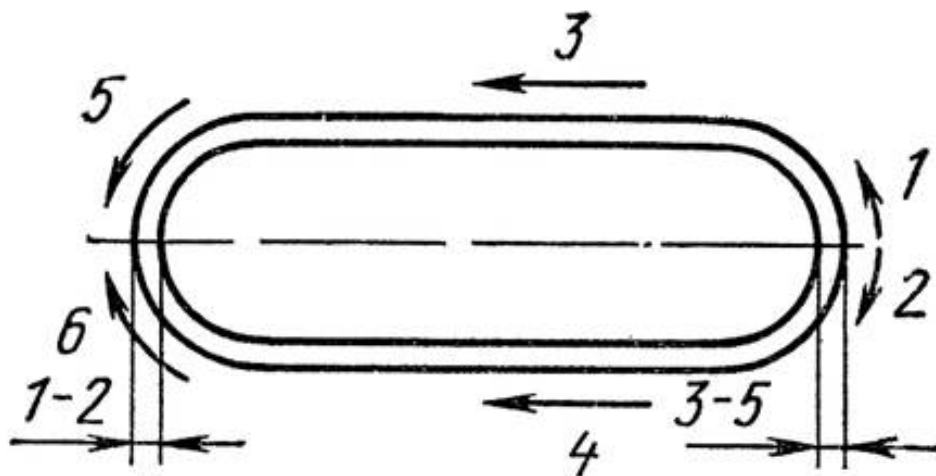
Последовательность выполнения сварного соединения при вварке заплата: 1, 2, 3, 4, 5, 6 – очередность заварки швов
